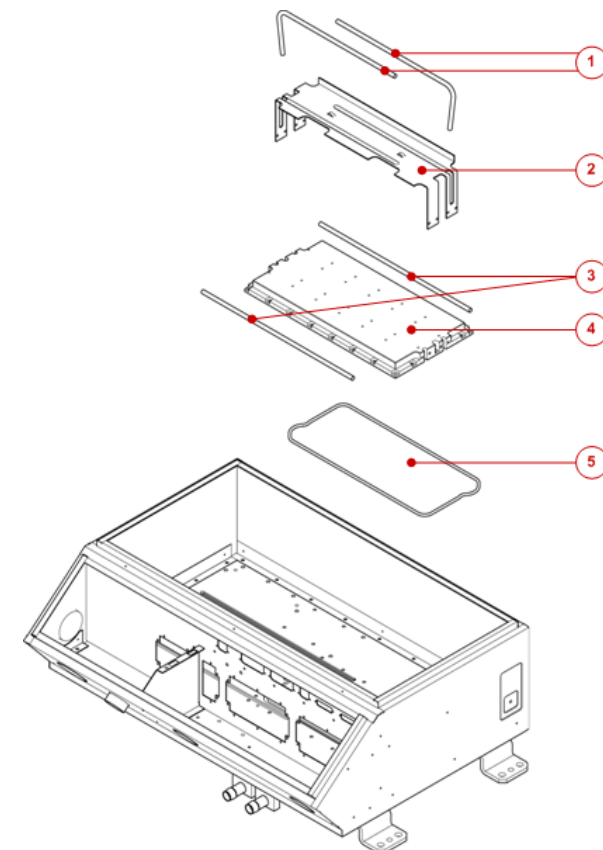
Explosionszeichnung Kühlsystem Komponenten / Exploded view of the components of the cooling system
